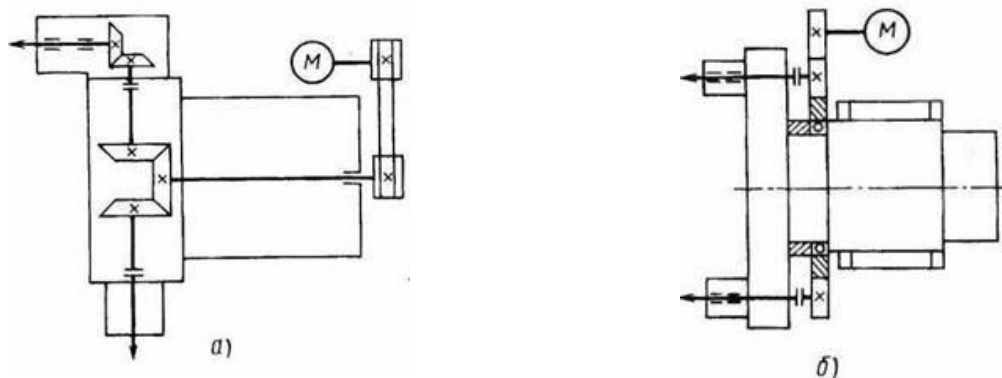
Револьверные головки токарных модулей с вращающимся инструментом
